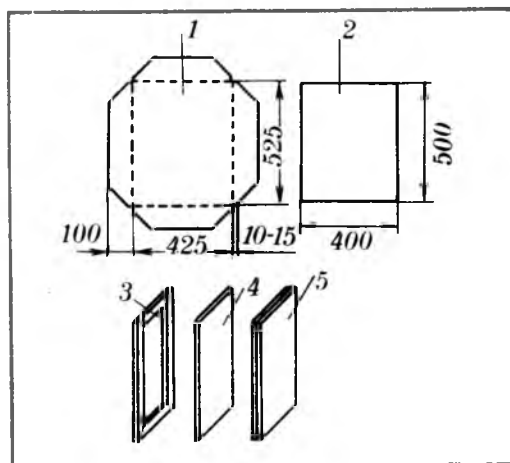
Основные элементы дверки верхнего отделения: 1 — облицовочное полотно с лицевой стороны; 2 — облицовочное полотно с тыльной стороны; 3 — рамка; 4 — облицованная заготовка; 5 — дверки
